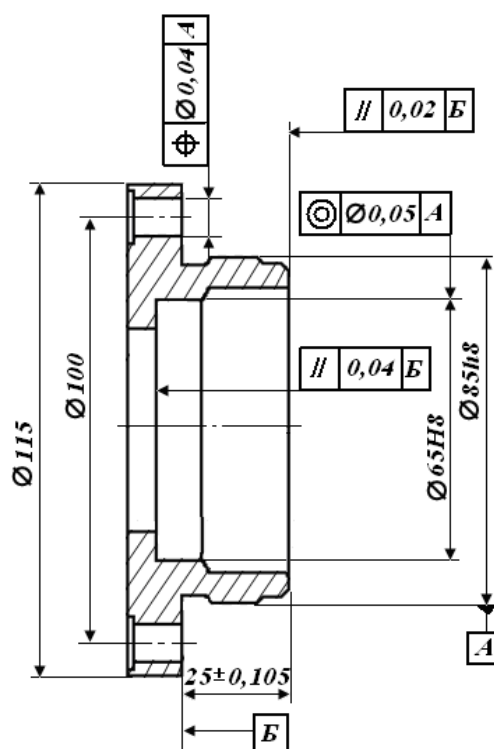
Ескіз кришки з зазначенням баз, допусків форми і розташування поверхонь
